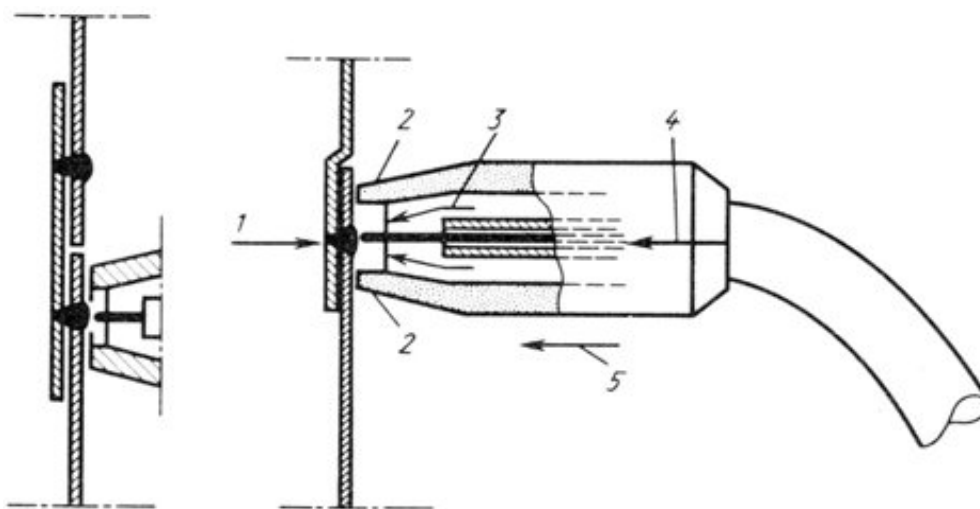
Точечная сварка тонких листов, один из которых выполнен с накладной лентой, а другой с отбортовкой: 1 – сварная точка; 2 – мундштук; 3 – защитный газ; 4 – размотка с выдержкой времени; 5 – небольшое усилие сжатия
